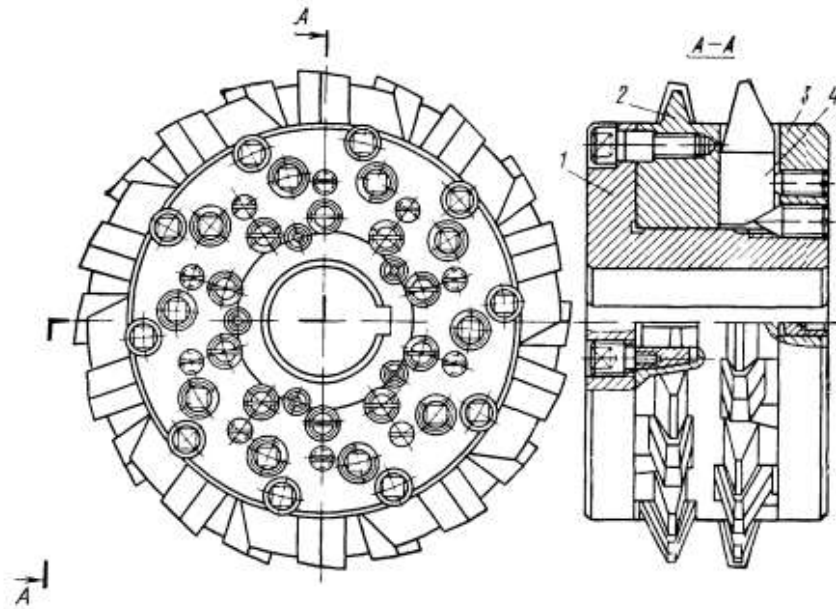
Диска дворядна чорнова фреза [5]
